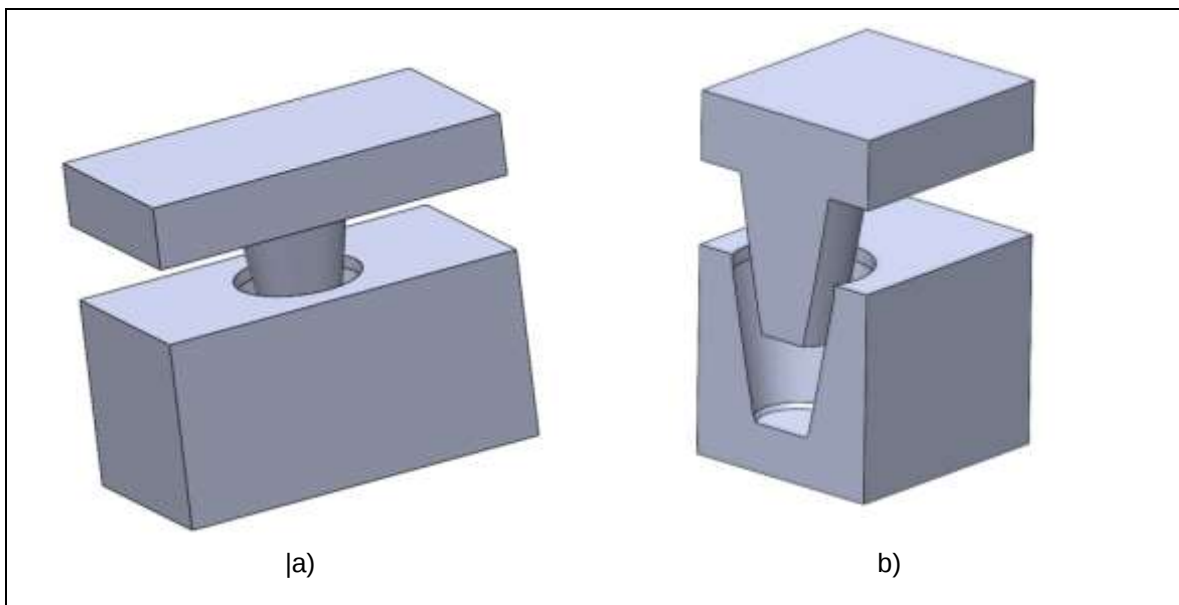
Vista 3D de ensamble del lado A y B para vaso en software SolidWords, a) Vista frontal, b) Vista corte transversal.
